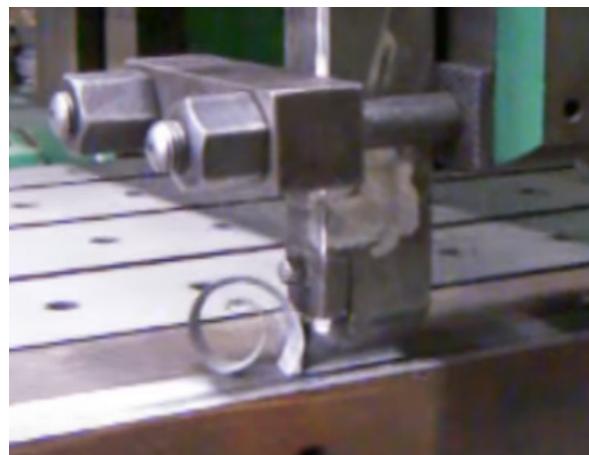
Strojna obrada piljenjem (Stock Photo ID: 1171723873)
